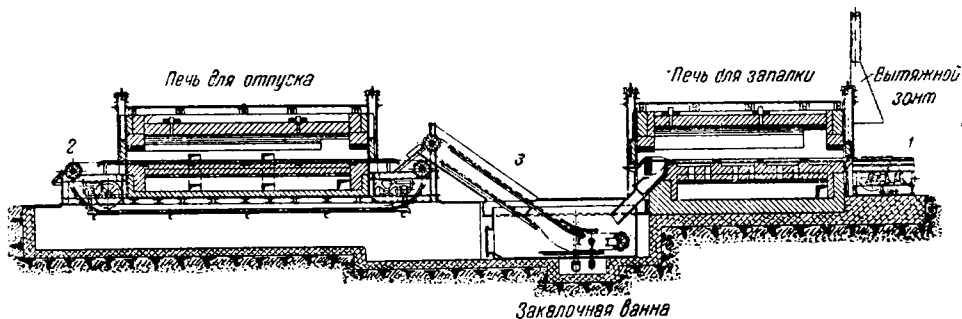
Агрегат для нагрева под закалку и отпуск непрерывного действия.
